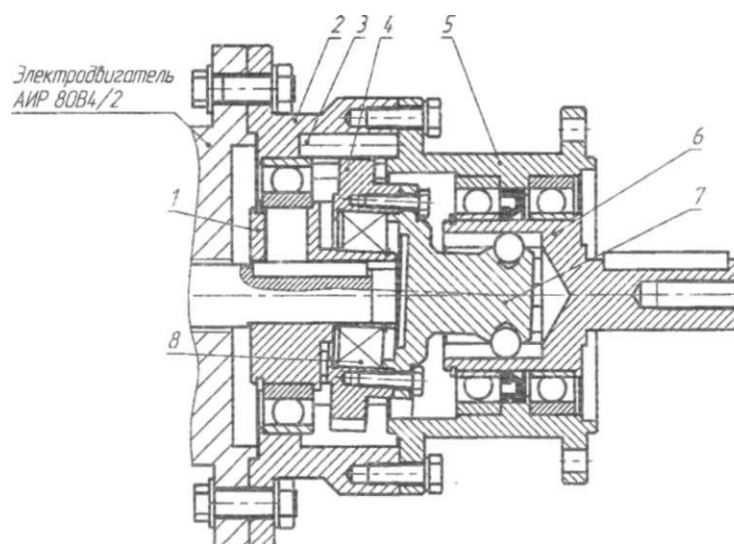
Общий вид конструкции прецессионного мотор-редуктора:
